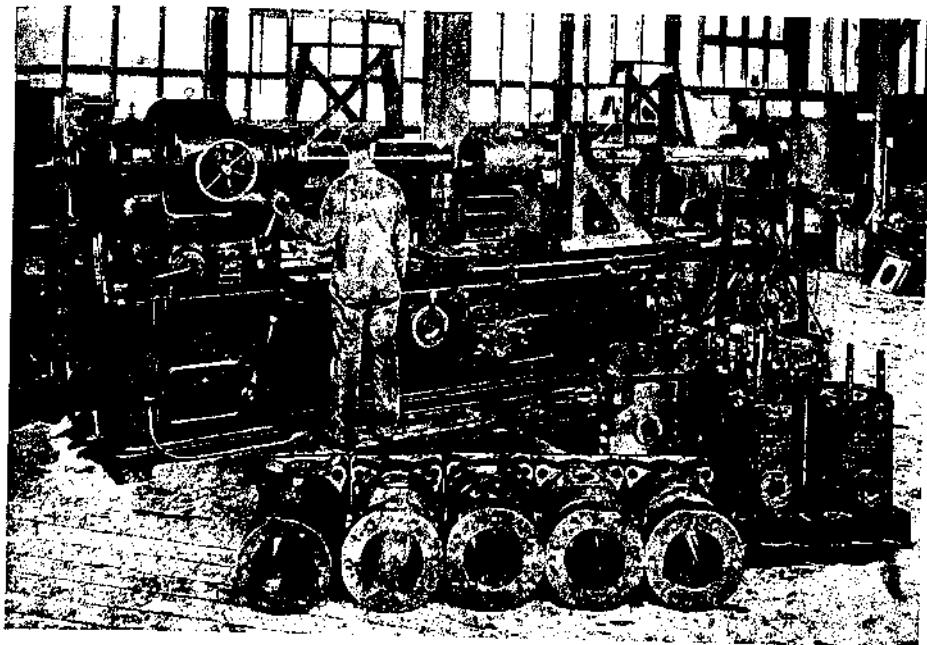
Шлифовка цилиндров двигателей Дизеля.
